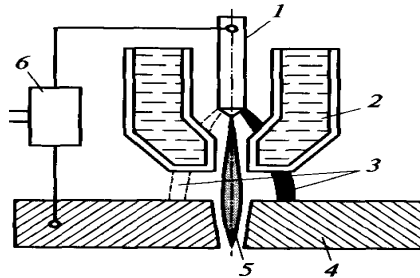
Схема подвійної дуги при плазово-дуговому зварюванні:
